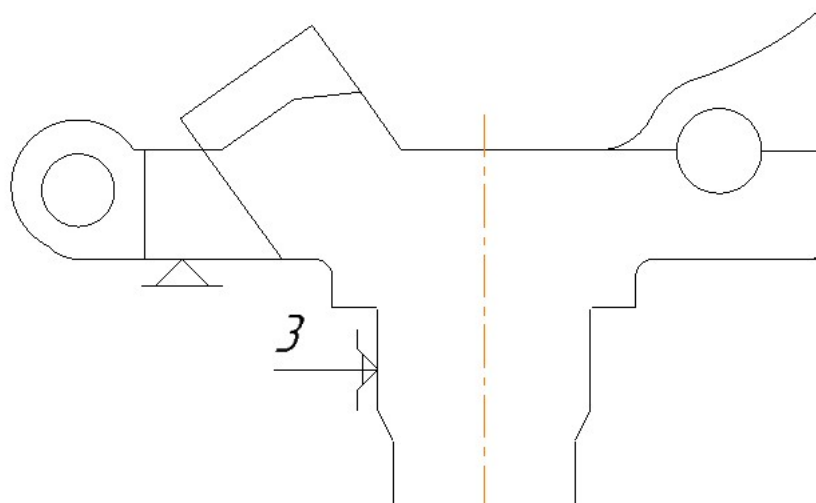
Схема базування деталі, що обробляється в пристрої
